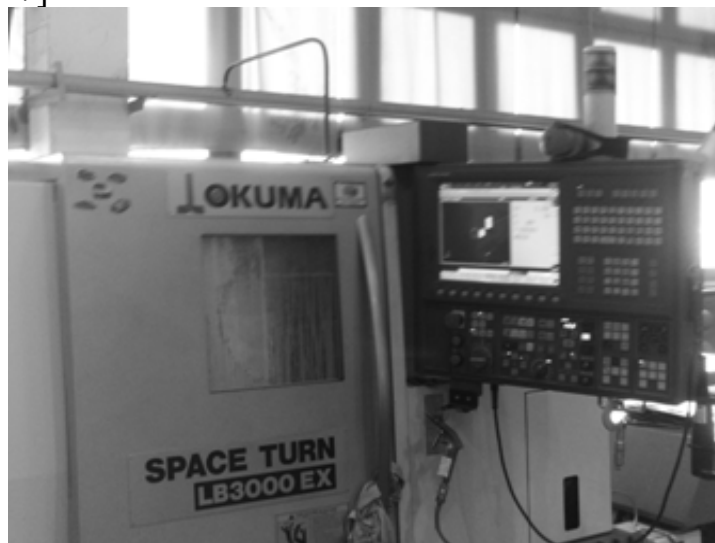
Верстат – Оброблювальний Центр SPACE TURN LB 3000EX
